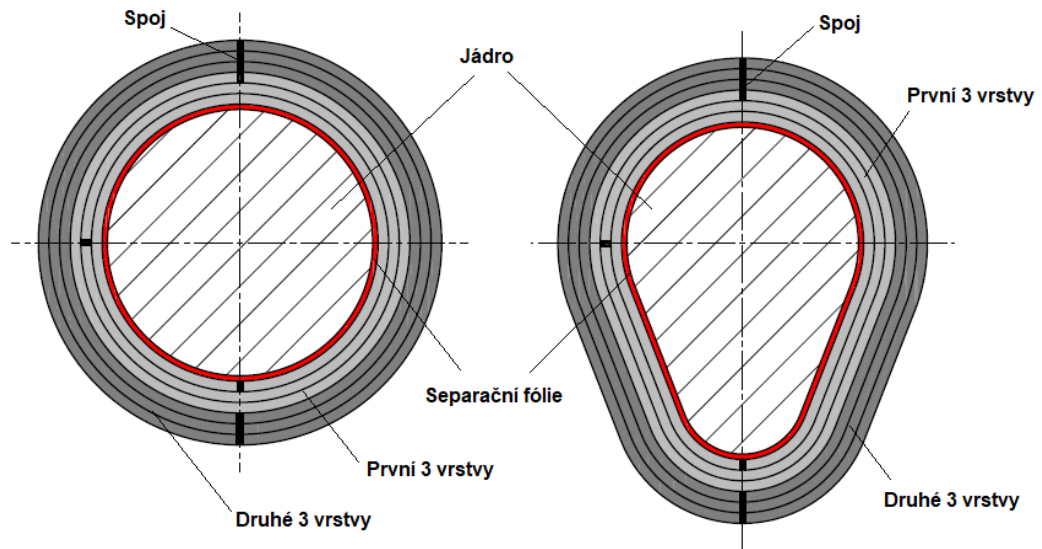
Zkušební tělesa Typ 1. uzavřeny ve formě.
